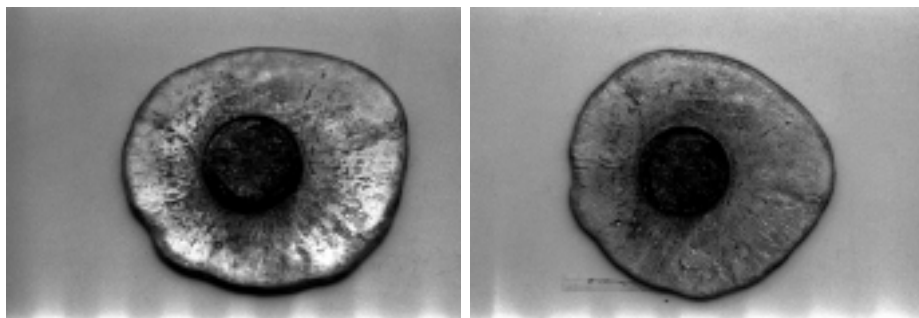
Vue de deux pièces injectées après modification du montage
